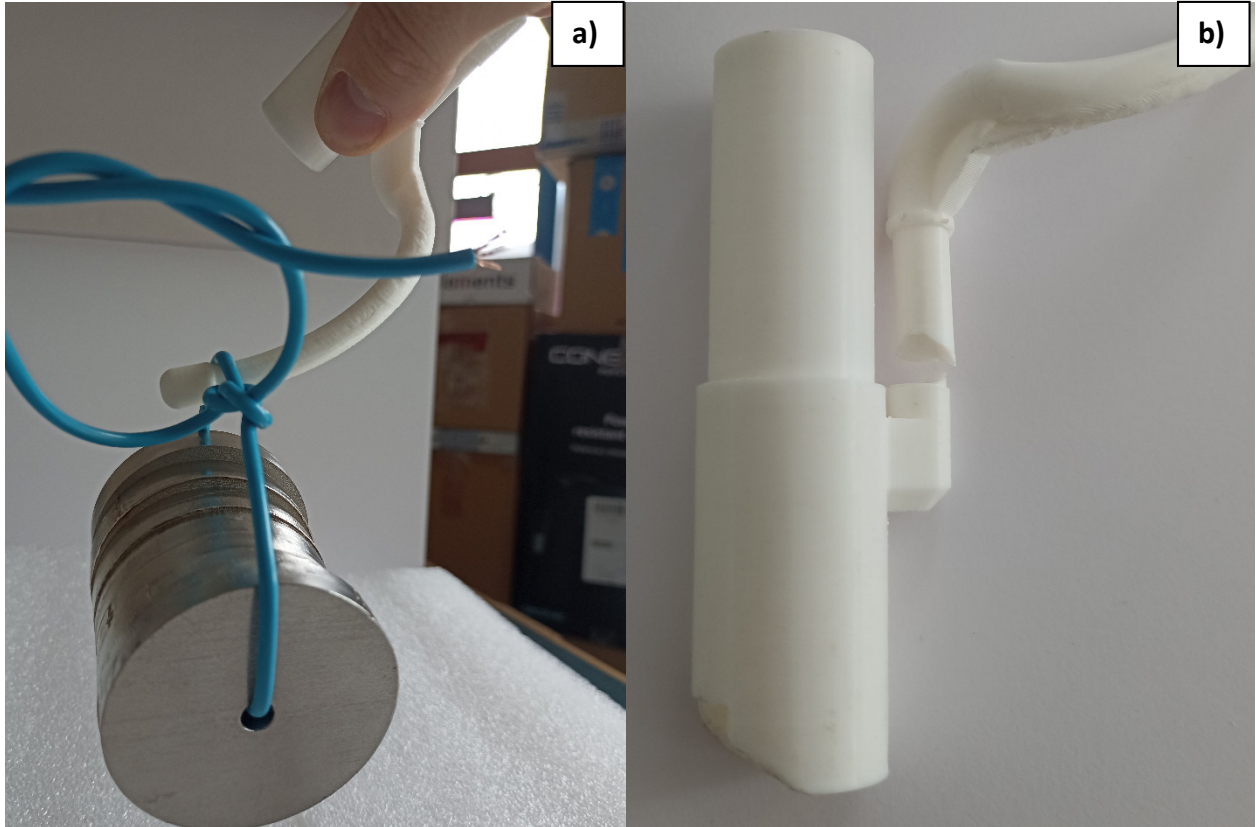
a) Momento del ensayo a 1,4 kg. b) Nueva zona de fractura.
